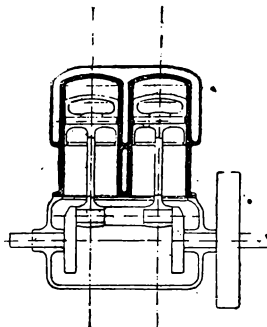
Motore a due cilindri con manovella a 360° cioè nel medesimo asse.
